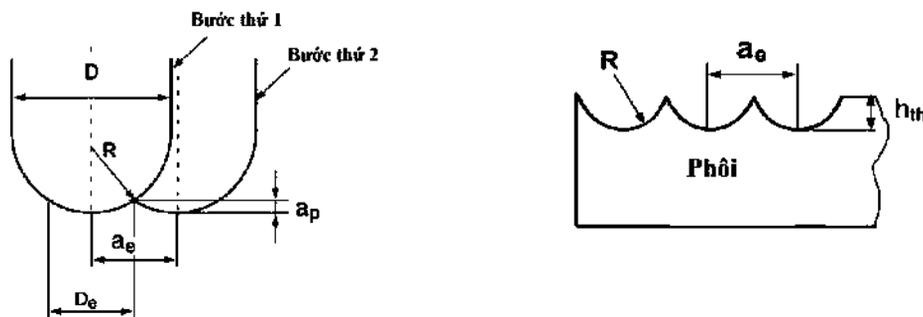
Геометрические параметры сфероцилиндрической фрезы и резания
